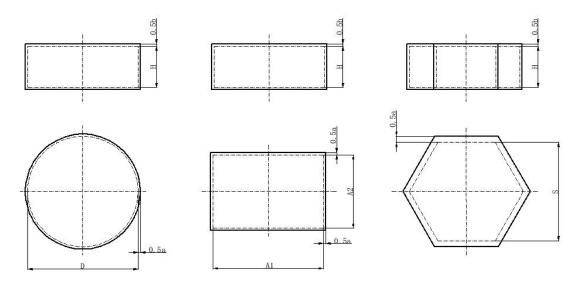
饼类及柱类钛合金锻件机械加工余量与公差
